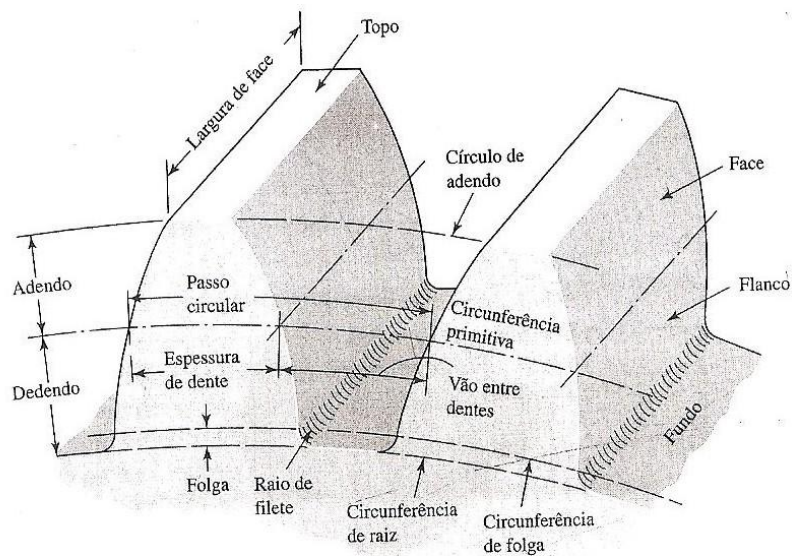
Nomenclatura de engrenagens cilíndricas (Shigley, 2006).
